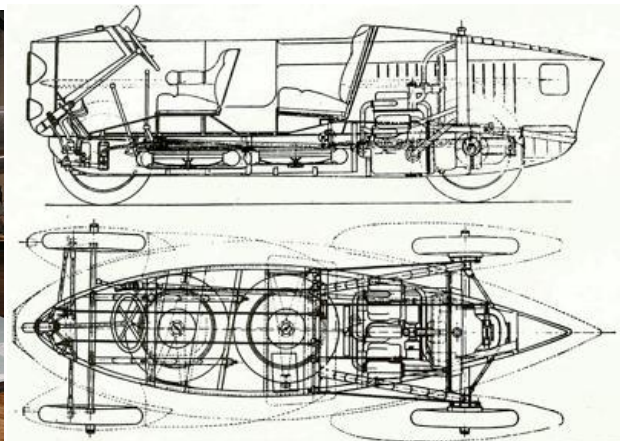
Vista planta y alzado del Rumpler Tropfenwagen [2]
